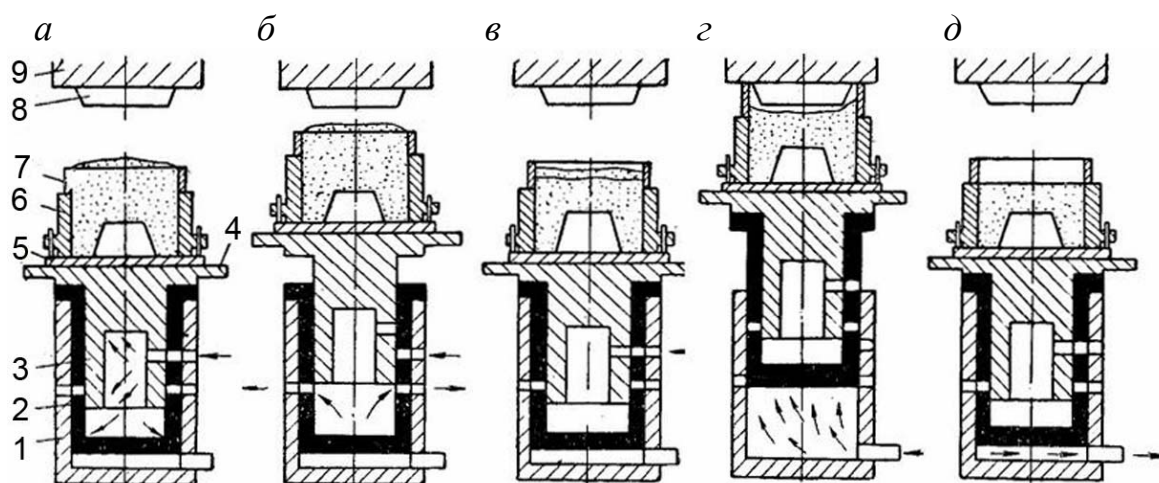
Процесс уплотнения смеси на встряхивающей машине с допрессовкой:
